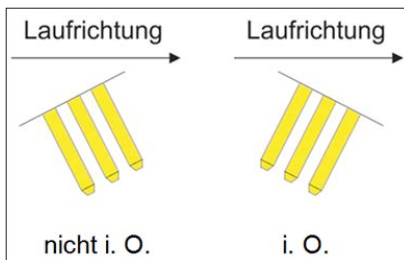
Laufrichtung bei schrägem Kontaktdesign
